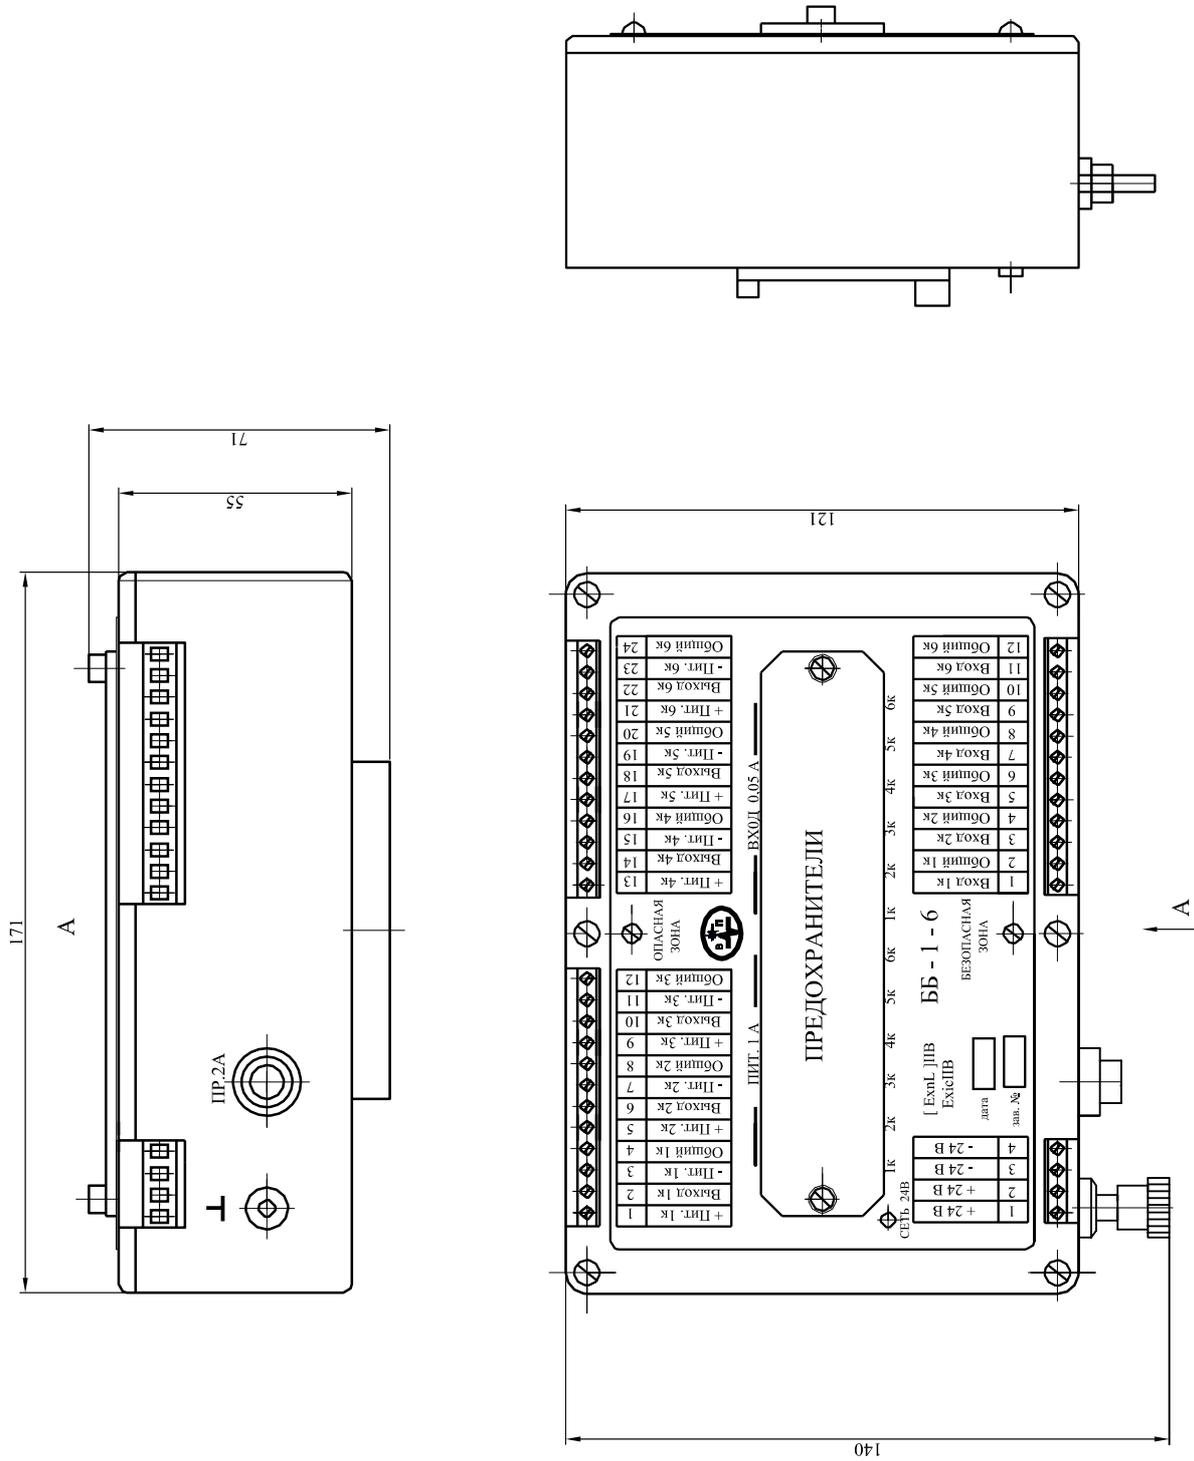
Габаритно-установочные размеры корпуса монтажного КМ-4
